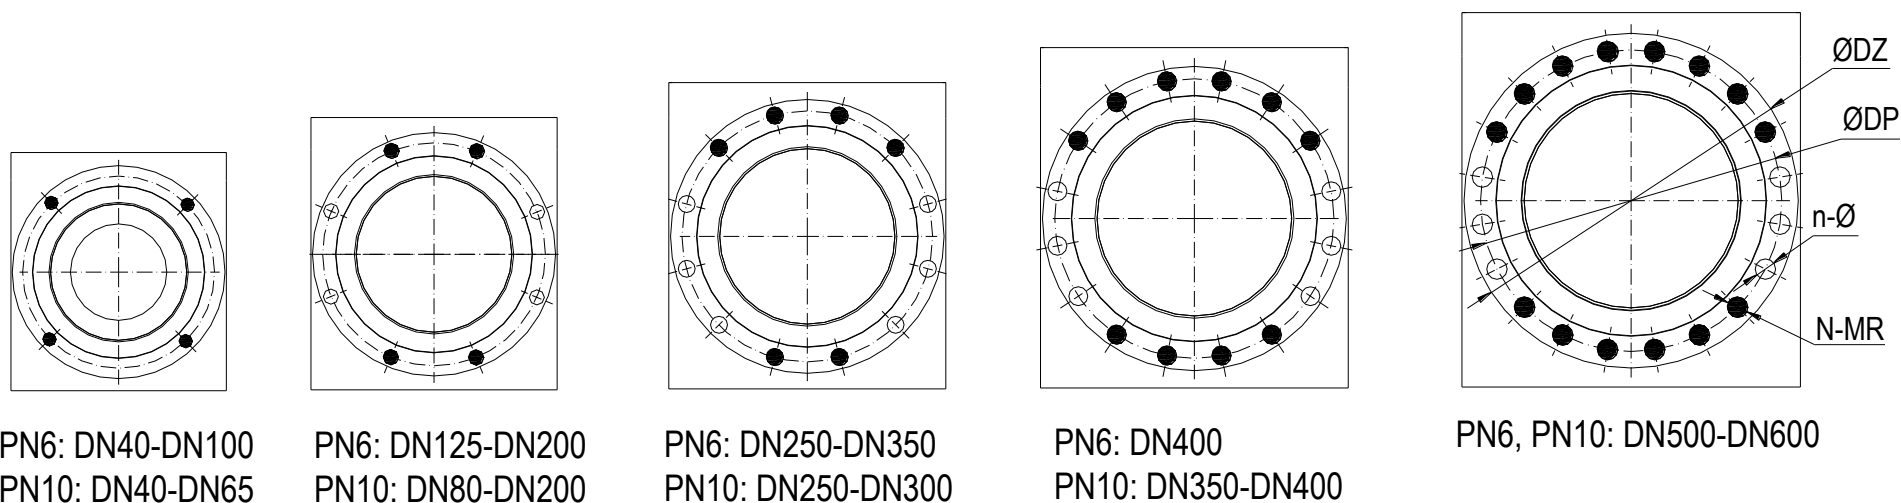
Główne wymiary urządzenia | Main device dimensions | Основные размеры устройства
